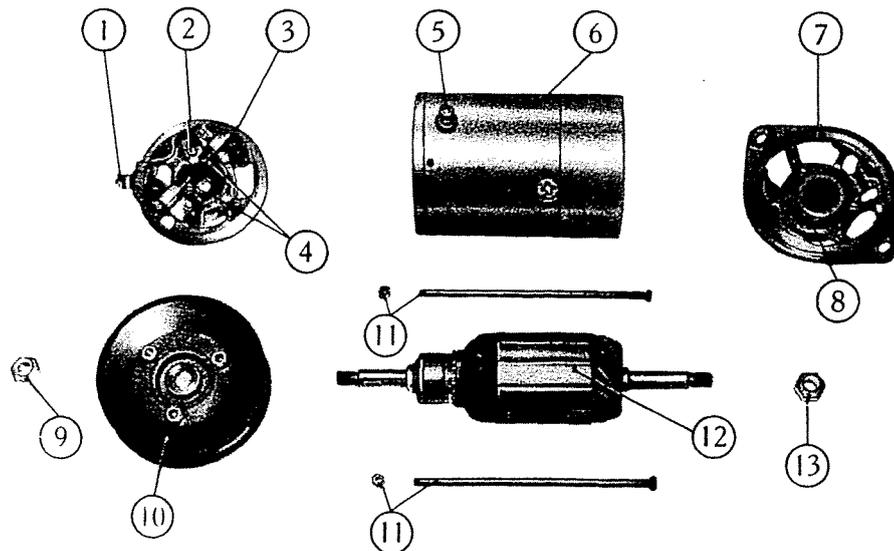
Bestandteile der Lichtmaschine R 90-180/12-2500 Spec. (bis Motor-Nr. 056195).
